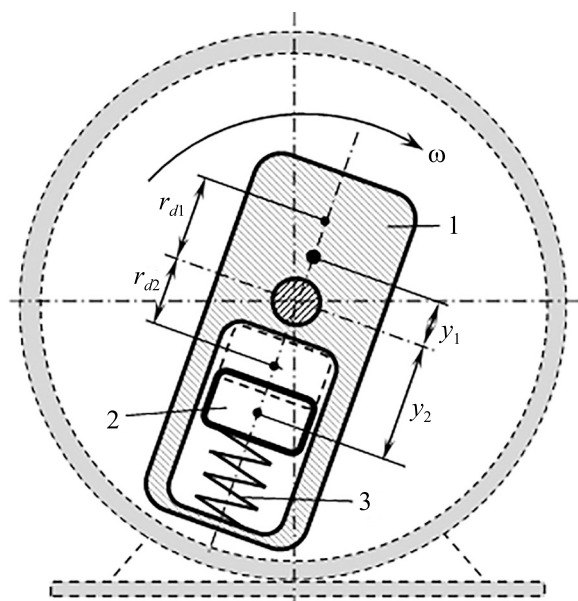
Саморегулируемый центробежный вибровозбудитель
